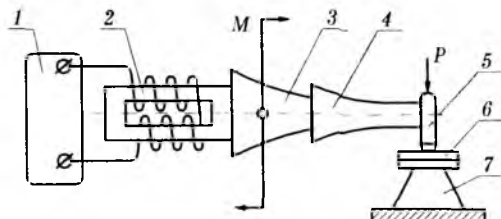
Схема ультразвуковой сварки:
